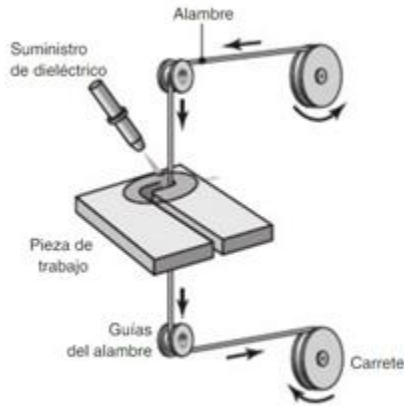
Esquema simple de una máquina de un proceso de corte por hilo.
